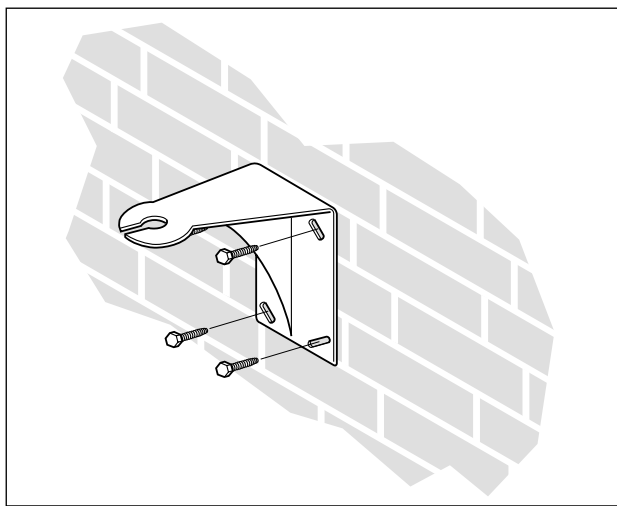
Attacco della staffa di montaggio a parete alla parete
